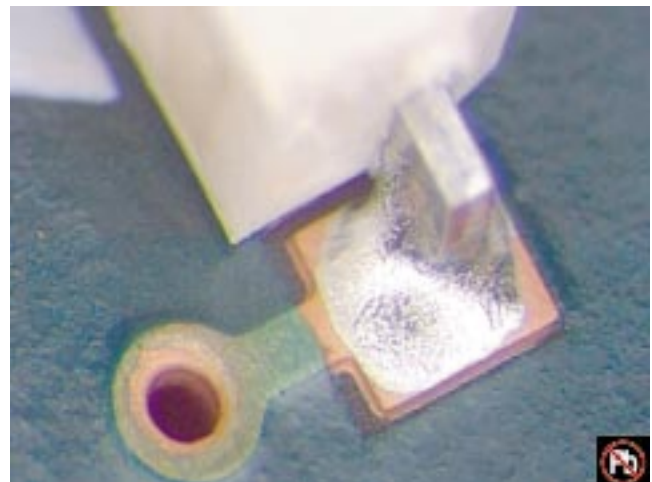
Soldadura SnAgCu Solder; Acabado OSP
